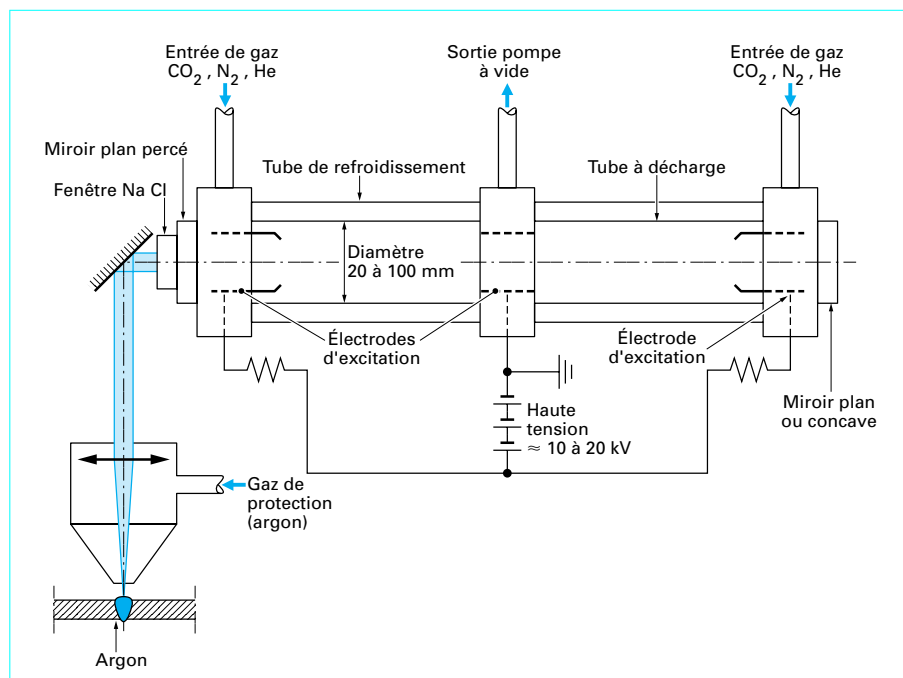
Principe du laser à dioxyde de carbone (CO₂, N₂, He) utilisé en soudage, d'après [17]
